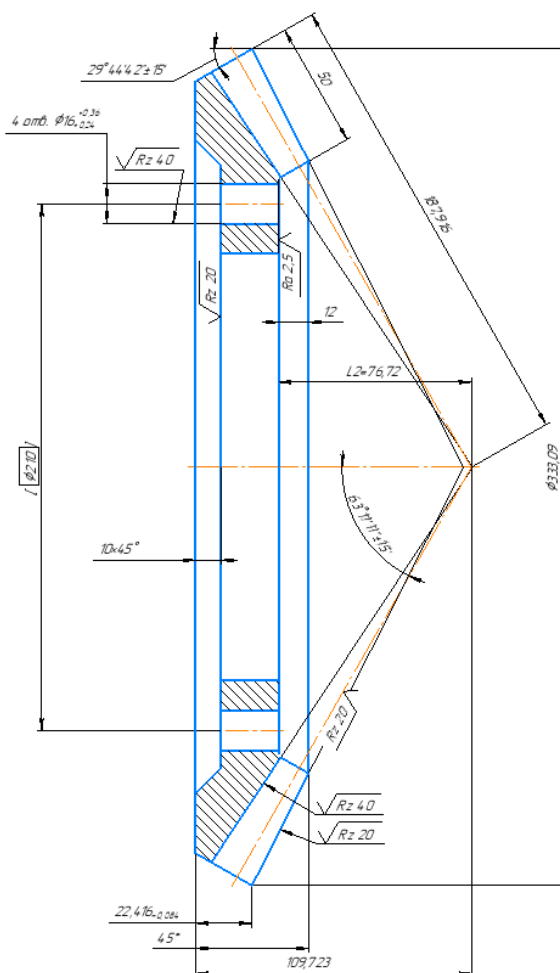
Ведомая Шестерня конического редуктора ДТ-30
